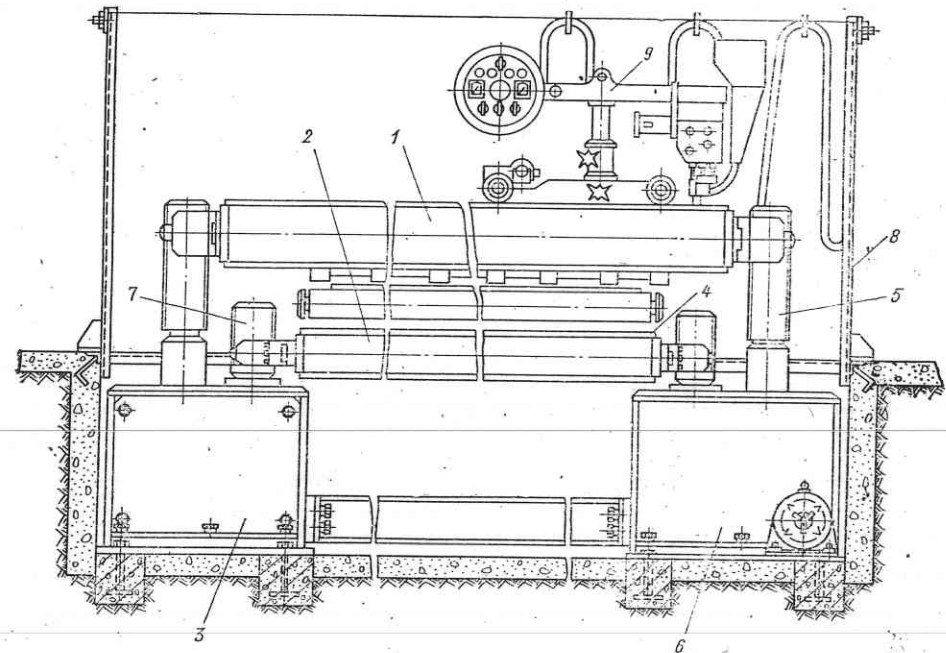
Установка для автоматической односторонней сварки под флюсом: 1 — верхняя балка; 2 — нижняя балка; 3 — левый механизм прижатия; 4 — медная подкладка; 5 — винт перемещения верхней балки; 6 — правый механизм прижатия; 7 — винт перемещения нижней балки; 8 — кронштейн; 9 — сварочный автомат
